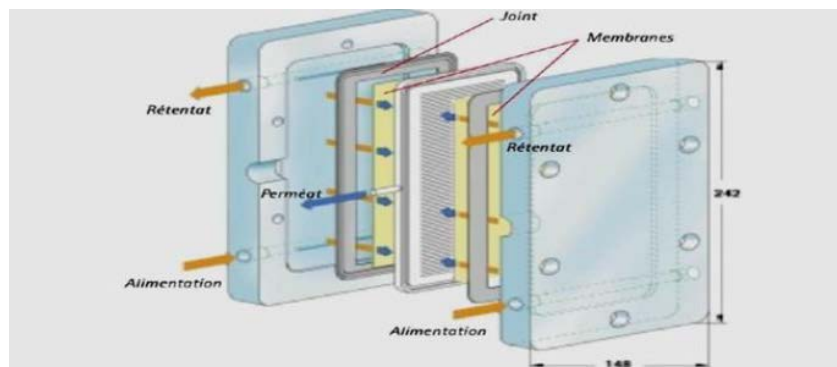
Module plan. Schéma d'un montage de type filtre-presse [55].
